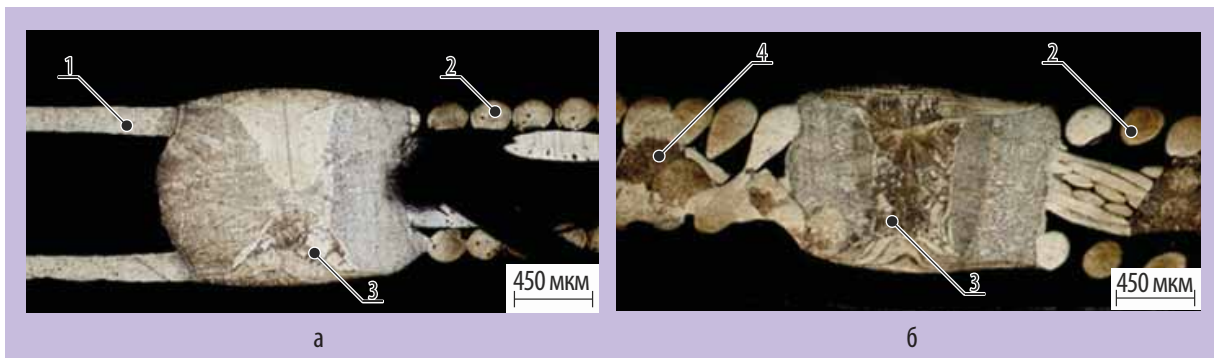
Структура сварного соединения корпуса с тросом (а) и частей троса (б) между собой, выполненного лазерной сваркой: 1 — корпус; 2 — гибкий трос; 3 — сварной шов; 4 — жёсткий трос
